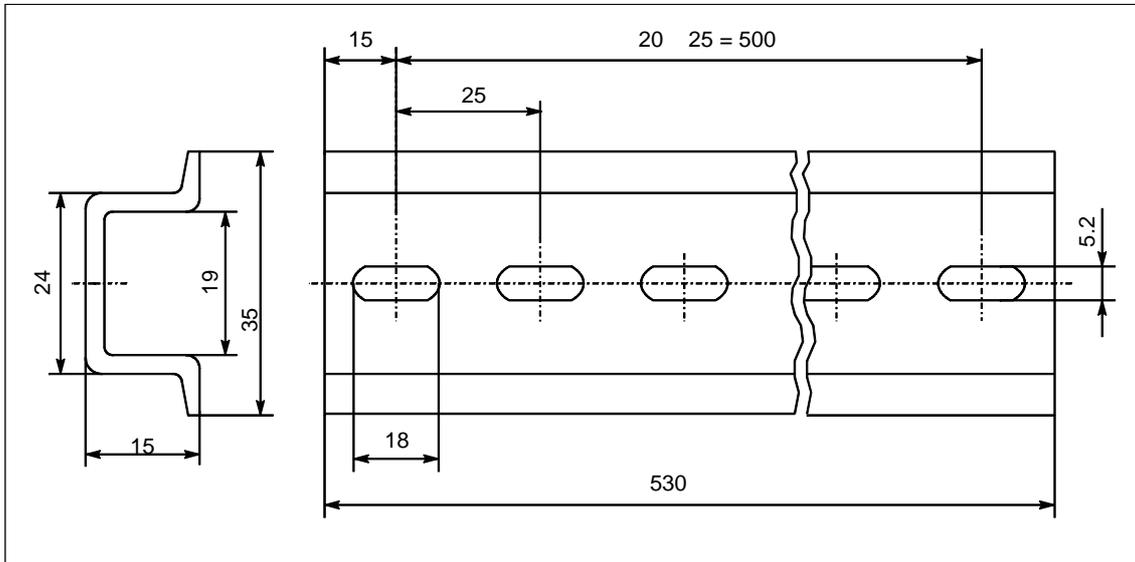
Чертеж с размерами 530-миллиметровой стандартной профильной шины
